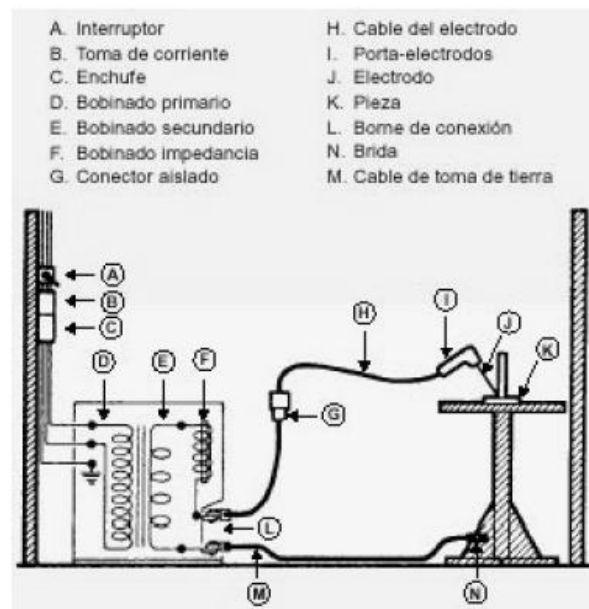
Instalación segura de un puesto de soldadura CA con transformador
